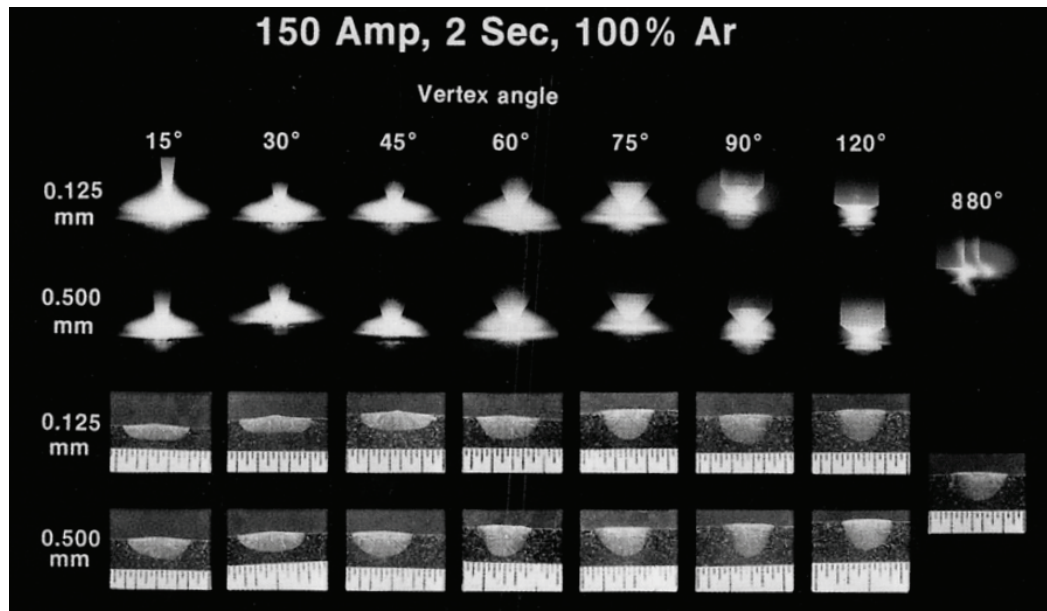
8 Forma del arco y perfil de soldadura como una función del ángulo de la punta del electrodo.
